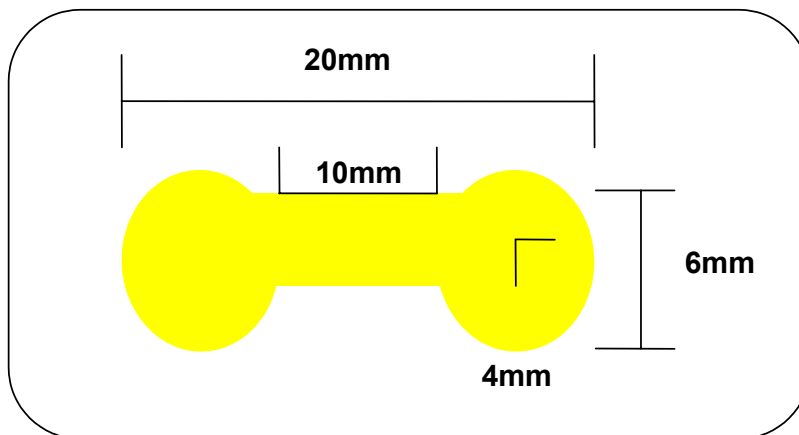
Desenho esquemático com as medidas do corpo de prova.
